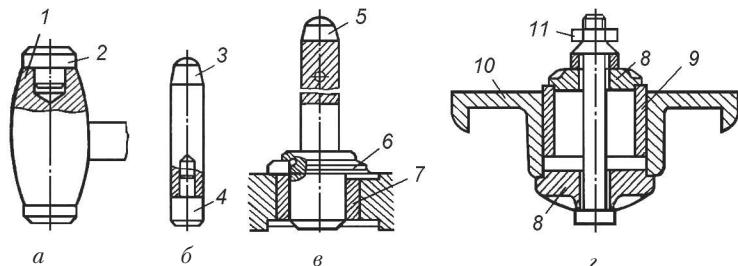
Інструменти та пристосування для складання пресових з'єднань:
